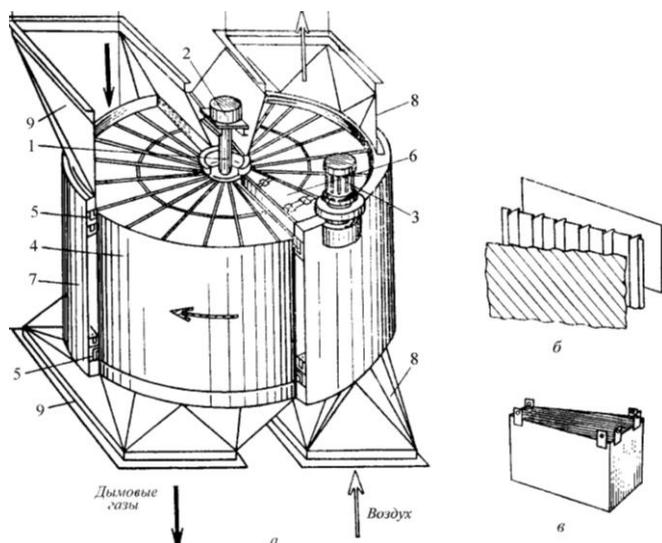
Регенеративный вращающийся воздухоподогреватель: *а* – внешний вид аппарата (передняя часть верхних коробов и кожуха условно отрезана); *б* – отдельные пластины набивки различной формы; *в* – секция с набивкой; 1 – вал ротора; 2 – верхний подшипник (нижний подпятник не виден на чертеже); 3 – электродвигатель с редуктором; 4 – ротор; 5 – наружное уплотнение; 6 – радиальное уплотнение; 7 – наружный кожух; 8, 9 – воздушные и газовые патрубки
